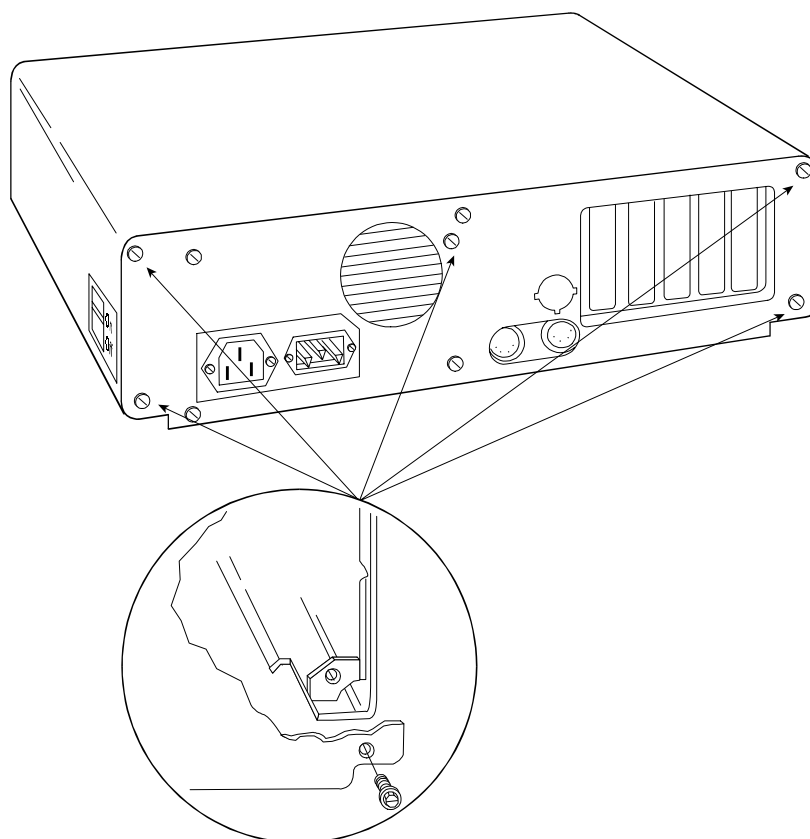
Местоположение винтов крепления на крышке корпуса для компьютеров класса XT
